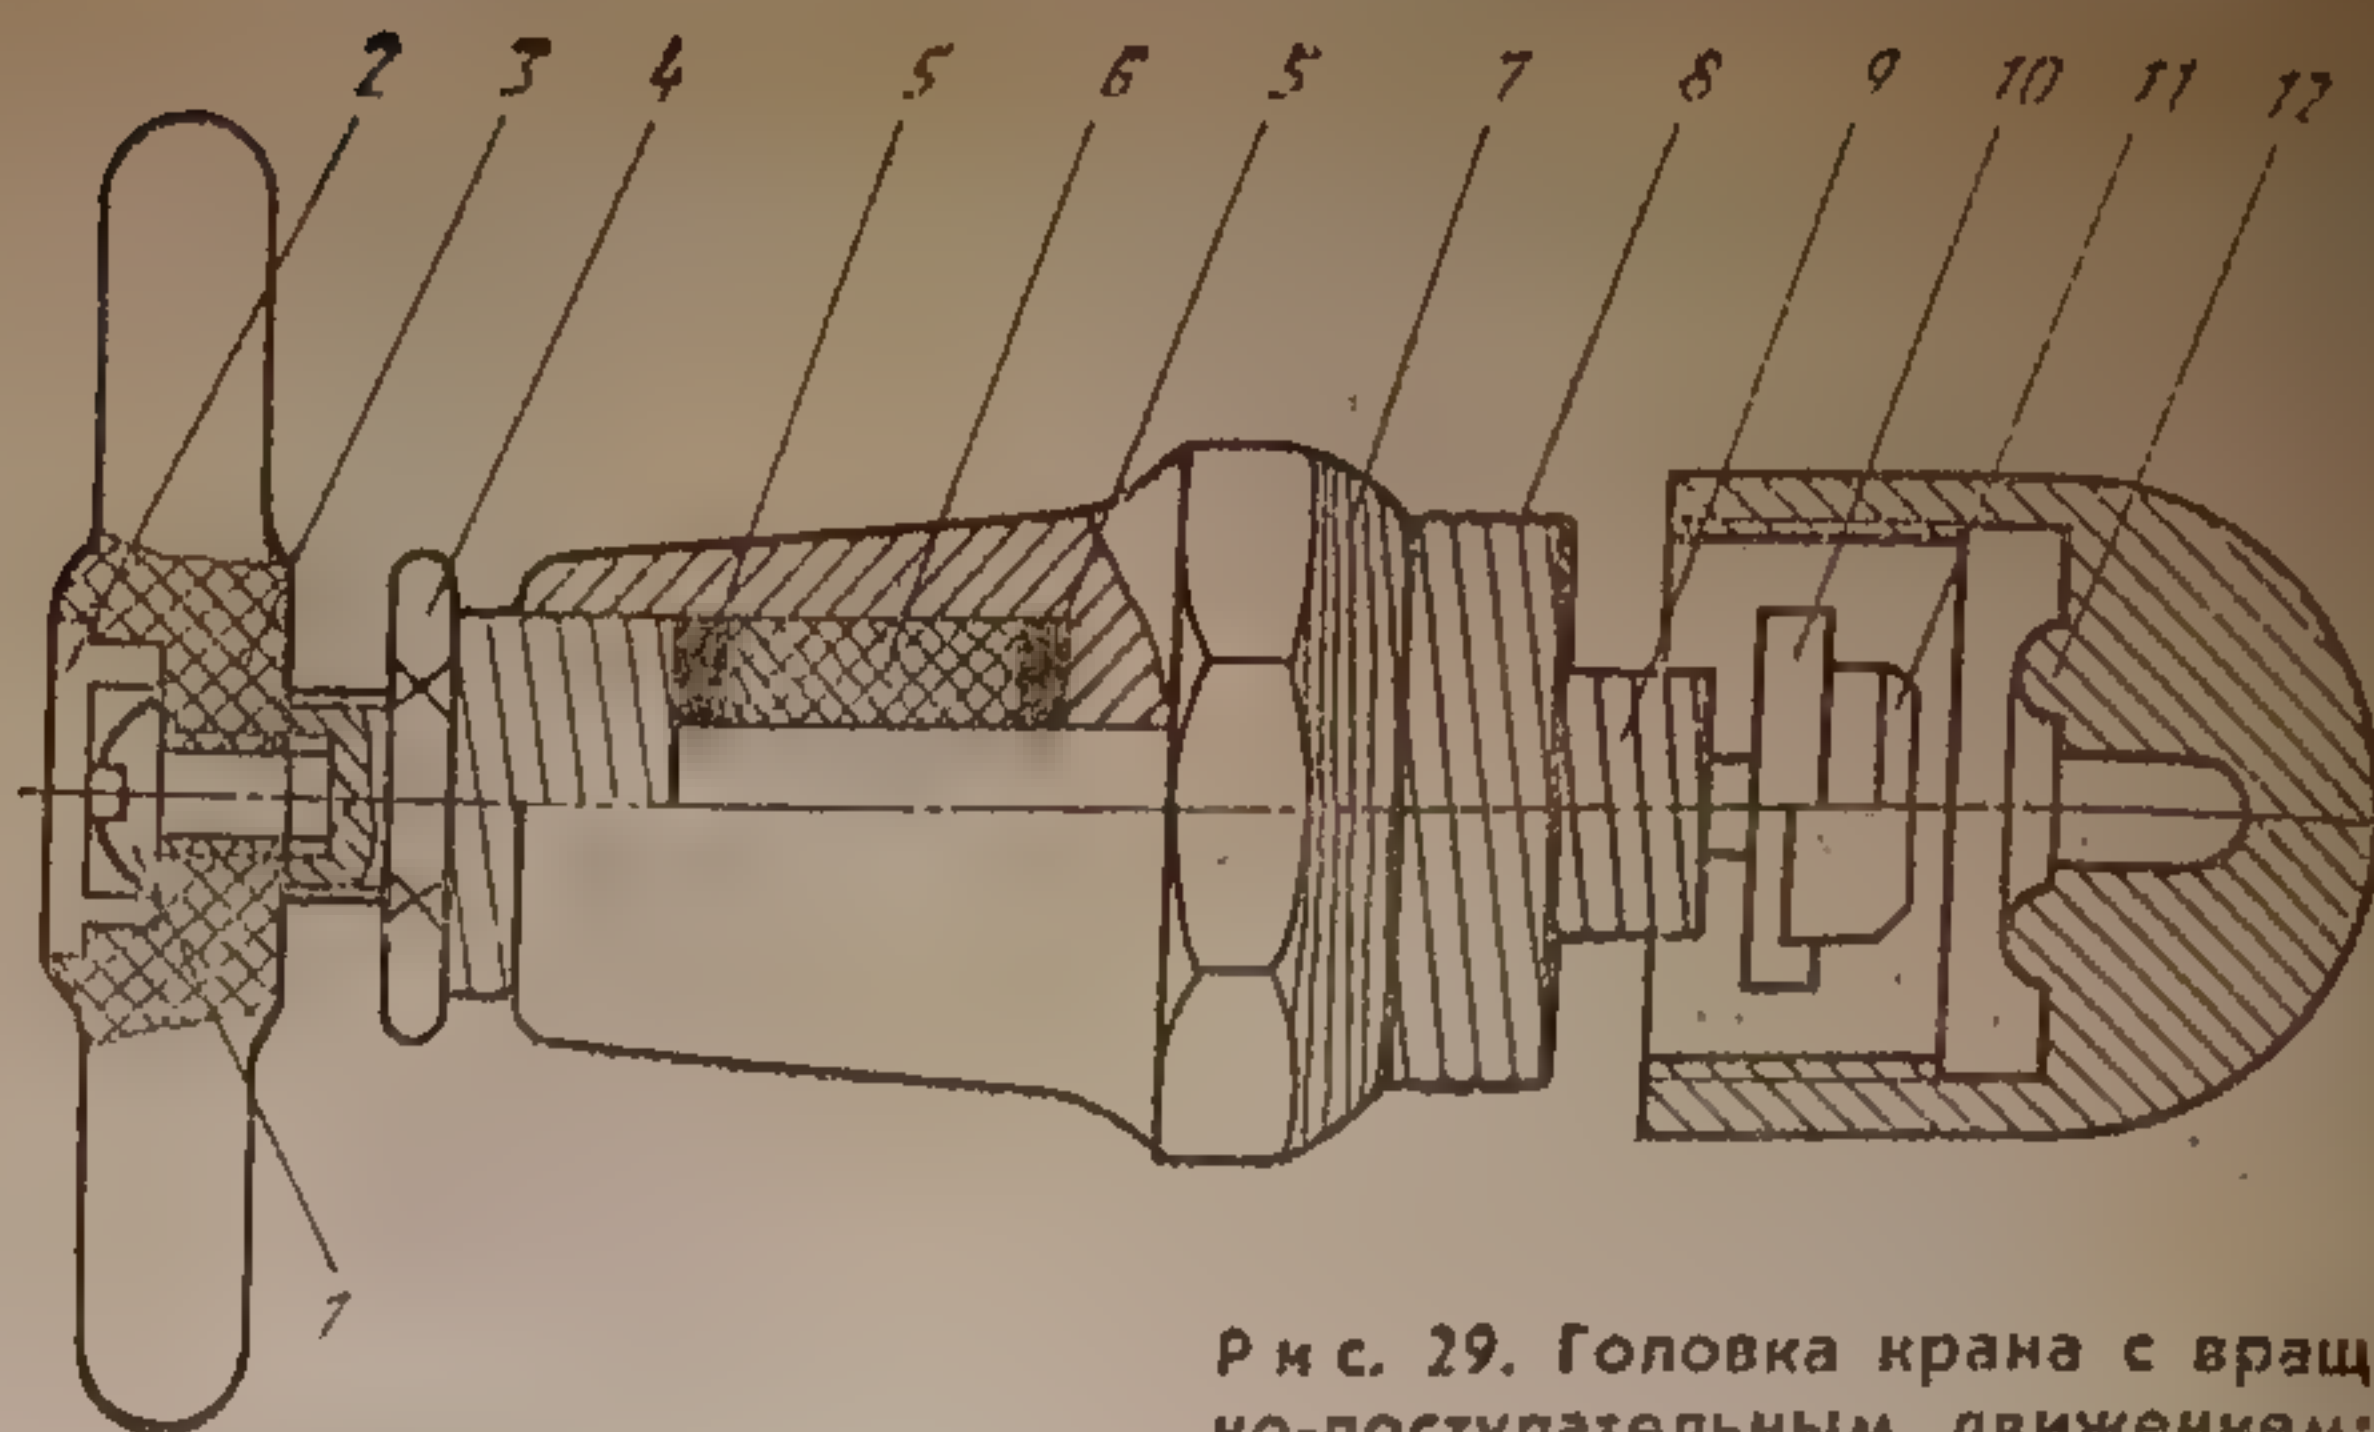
Головка крана с вращательно-поступательным движением: 1 — винт; 2 — указатель; 3 — маховик; 4 — втулка сальника; 5 — кольцо; 6 — сальник; 7 — уплотнение; 8 — корпус; 9 — шток; 10 — клапан; 11 — прокладка; 12 — седло корпуса крана или боковины смесителя
